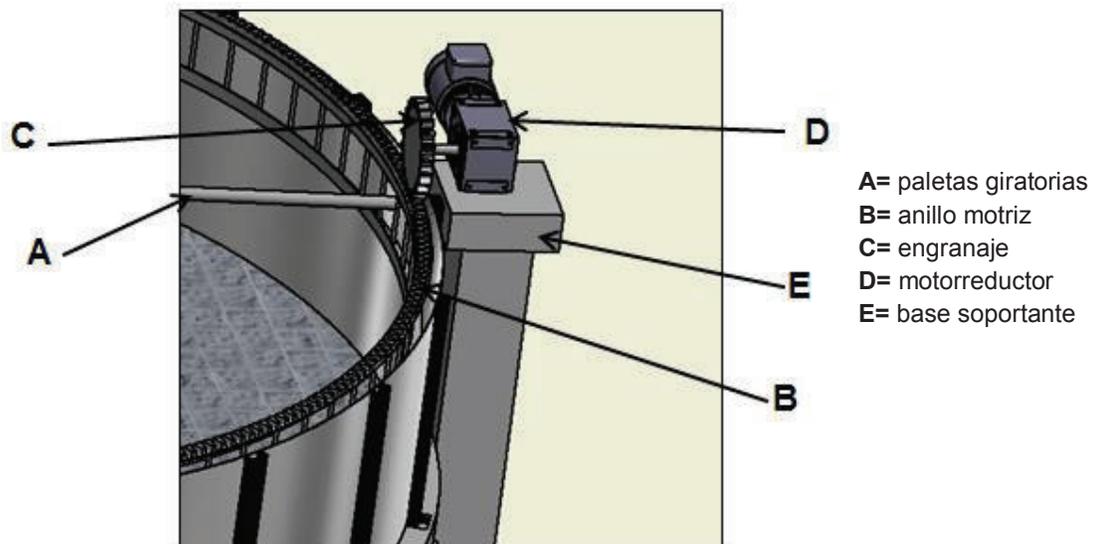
Partes Principales Alternativa III: Sistema motriz con engranajes y paletas agitadoras de grano.
